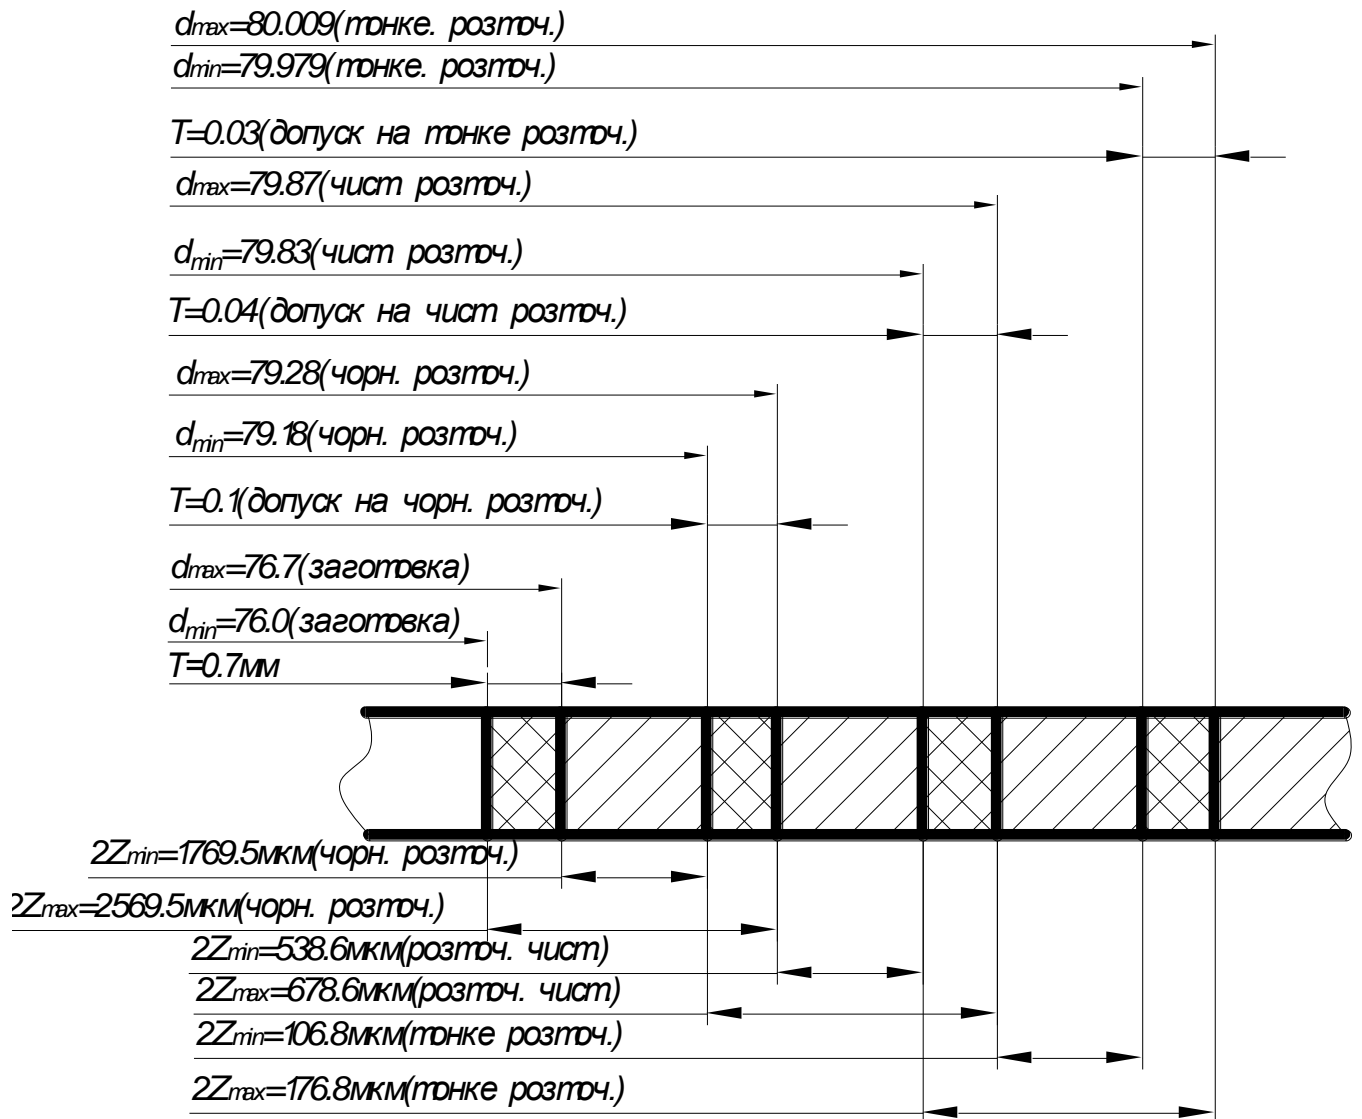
Схема припусків на обробку заготовки отвору $\varnothing 80K7$
